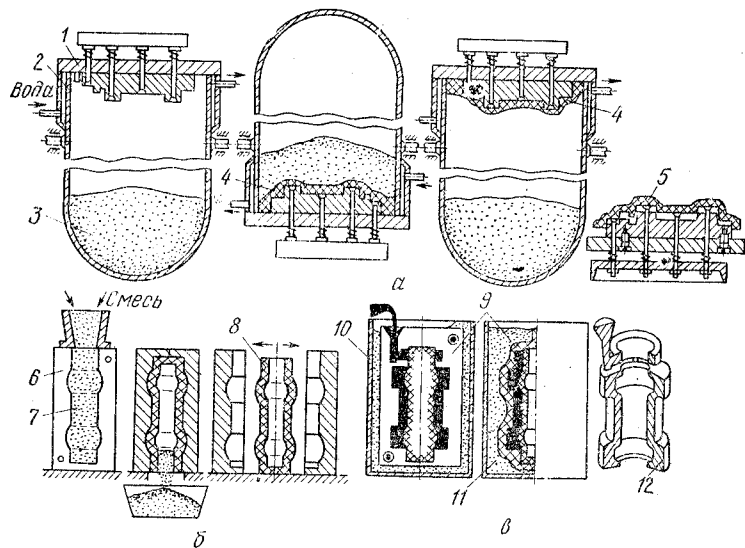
Схема процесса изготовления отливок методом литья в оболочковые формы
